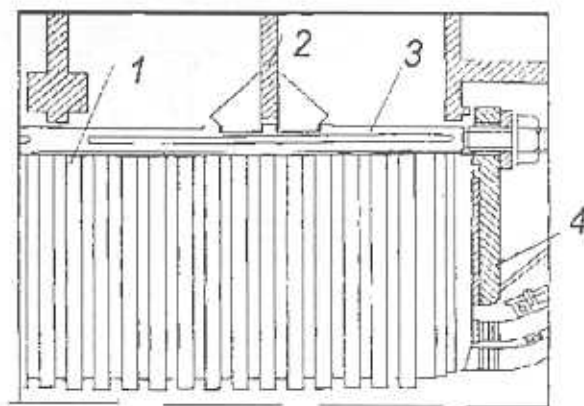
Эластичная подвеска сердечника в корпусе [3]:
